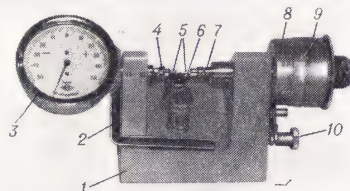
Настольный микрометр со стрелочным отсчётным устройством: 1 — корпус; 2 — арретир; 3 — отсчётное устройство; 4 — измерительный стержень отсчётного устройства; 5 — измерительные наконечники; 6 — столик; 7 — измерительный стержень микрометрической головки; 8 — стебель; 9 — барабан; 10 — стопор.
